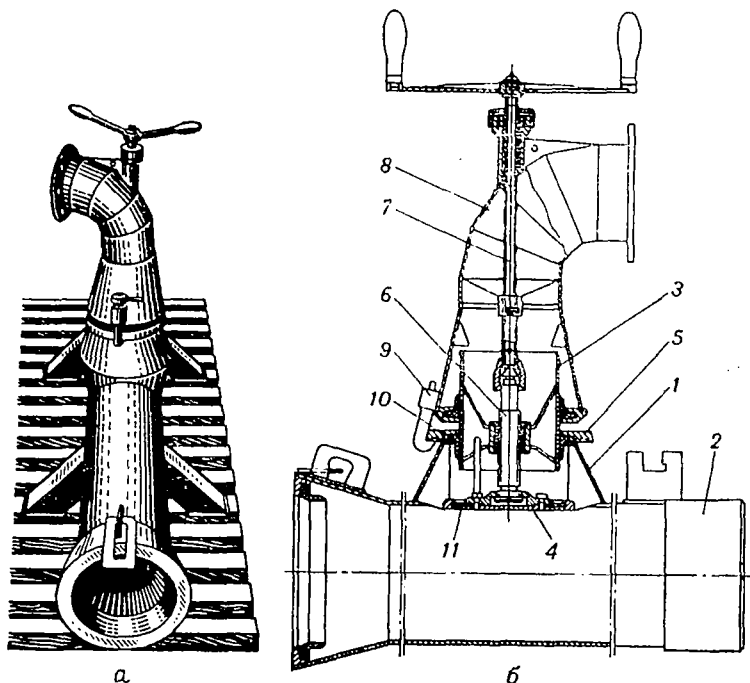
Гидрант-водовыпуск для разборных трубопроводов с подсоединенной к нему колонкой:
